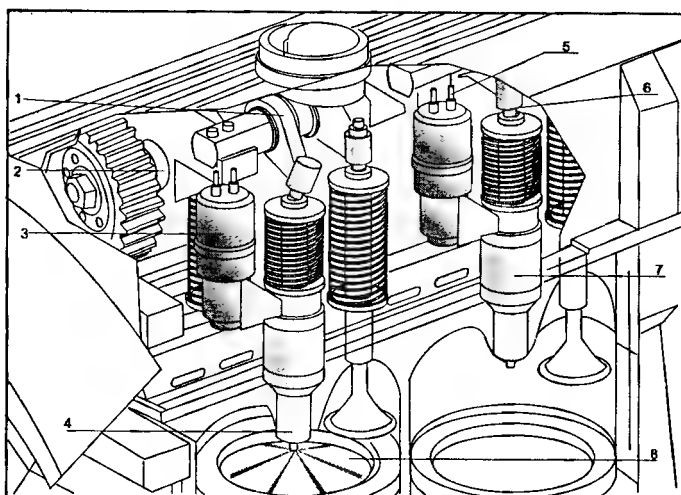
Конструкция системы впрыска с насос-форсунками UIS: 1 — коромысло привода UIS; 2 — распредвал двигателя; 3 — электромагнитный клапан UIS; 4 — распылитель UIS; 5 — разъем подключения UIS; 6 — плунжер UIS; 7 — корпус UIS; 8 — камера сгорания двигателя
